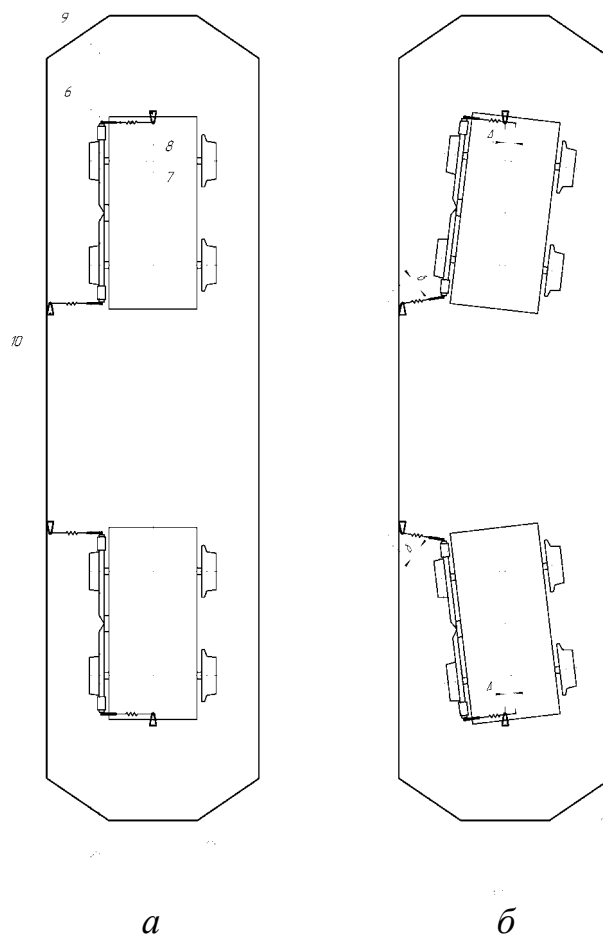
Загальний вигляд візка із гребнезмащувачем колеса
